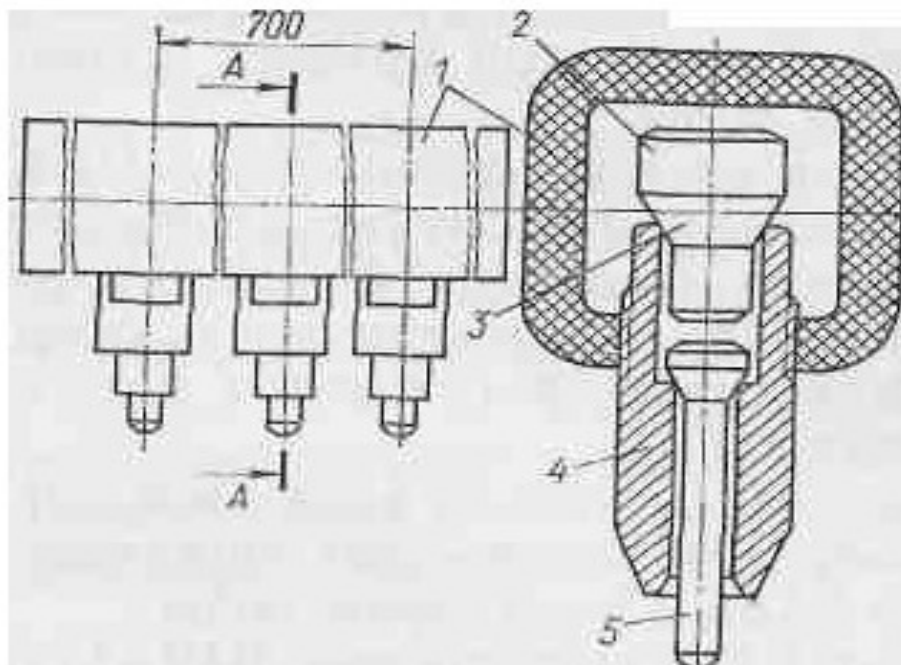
Напувалка ніпельна (краплинна): 1 - водовод; 2- верхній клапан; 3-фаски; 4 - корпус; 5 - нижній клапан.
